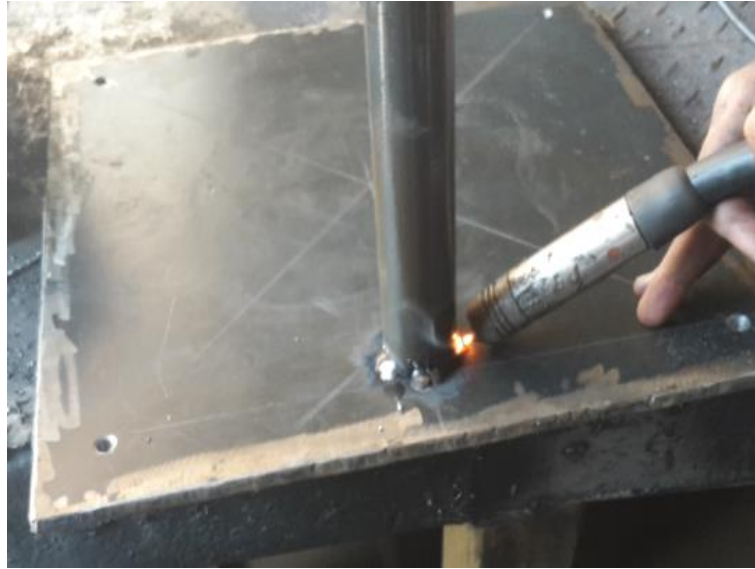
Tubo sendo soldado perpendicularmente a chapa.
